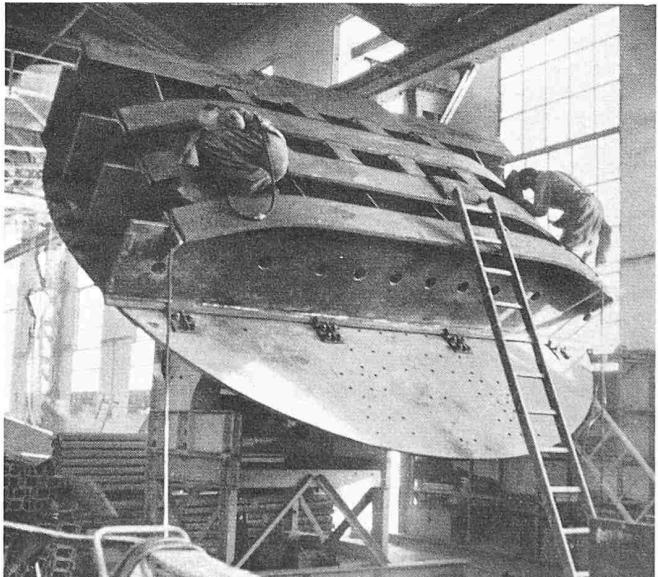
Teilstück zum Schweißen auf der Drehvorrichtung
